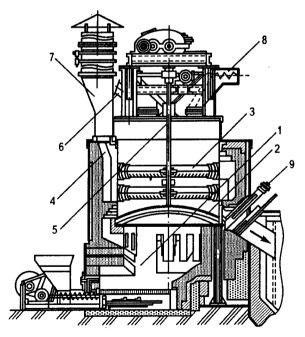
Схема гипсоварочного котла: 1 – топка; 2 – днище; 3 – жаровая труба; 4 – корпус котла; 5 – мешалка; 6 – патрубок для удаления пара; 7 – дымовая труба; 8 – загрузочный шнек; 9 – шибер; 10 – люк для разгрузки
